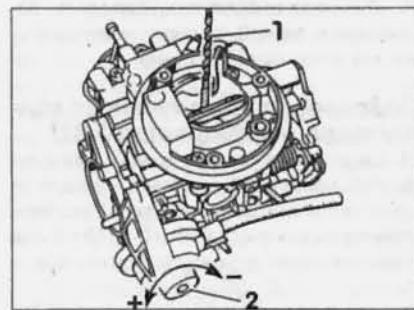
Проверка зазора воздушной заслонки сверлом (1) и регулировочный болт (2) - карбюратор 1B3 (Глава 11)
